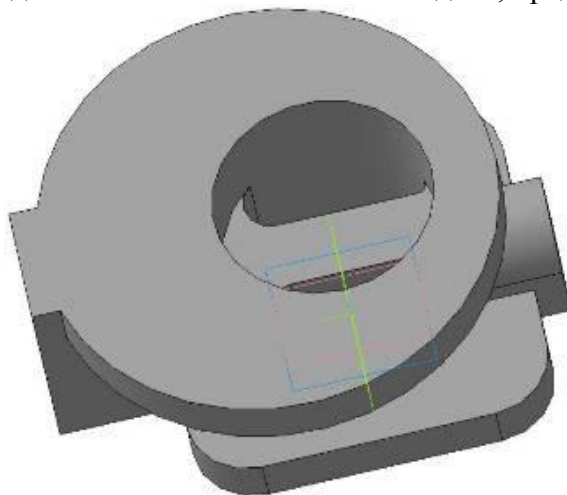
3D- модель заготовки корпуса датчика разряжения
